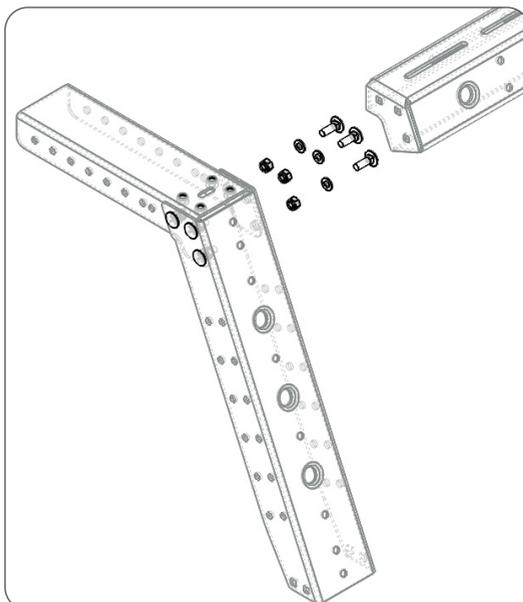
Ecksteher verschraubt mit Querstrebe / corner strut bolted together with cross strut
